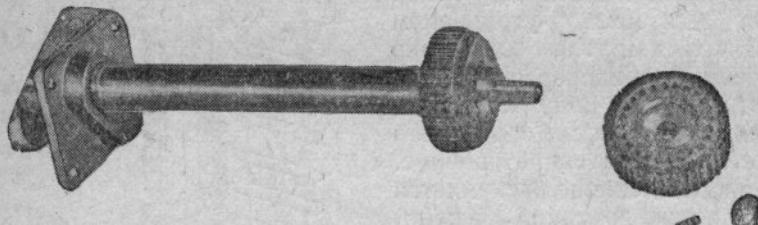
Выступающая из фонаря часть шпиндельного приспособления для подачи углей с рукоятками. На снятой крайней рукоятке видны отверстия под соединительный штифт
